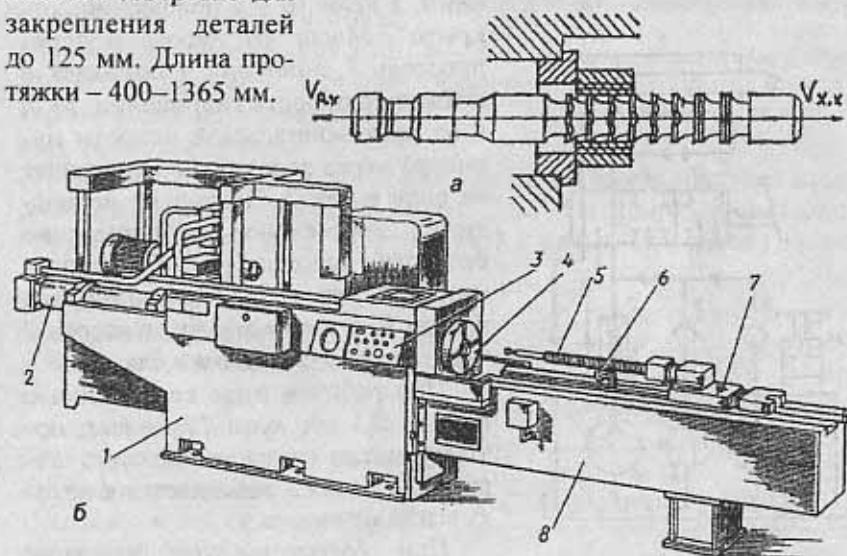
Схема протягивания (а) и общий вид (б) горизонтально-протяжного станка мод. 7523:
